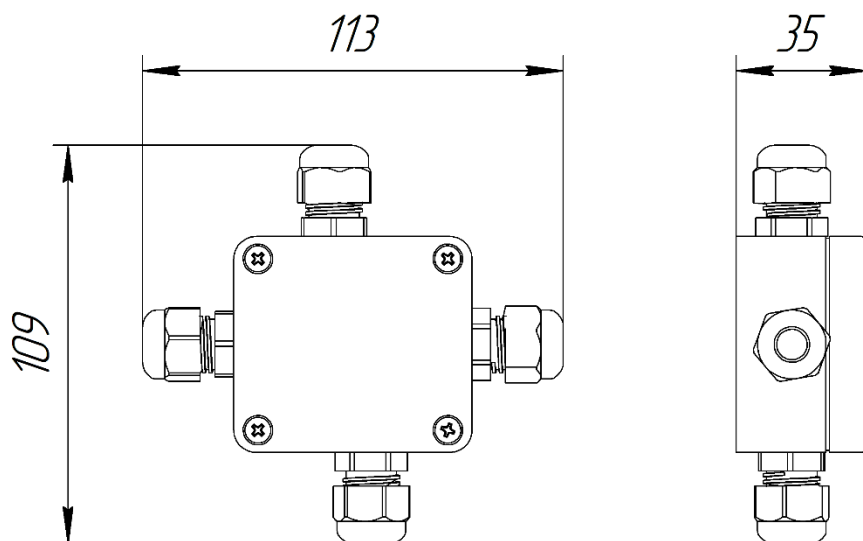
Габаритный чертеж разветвителя RS-SPLIT-4S-IP65
